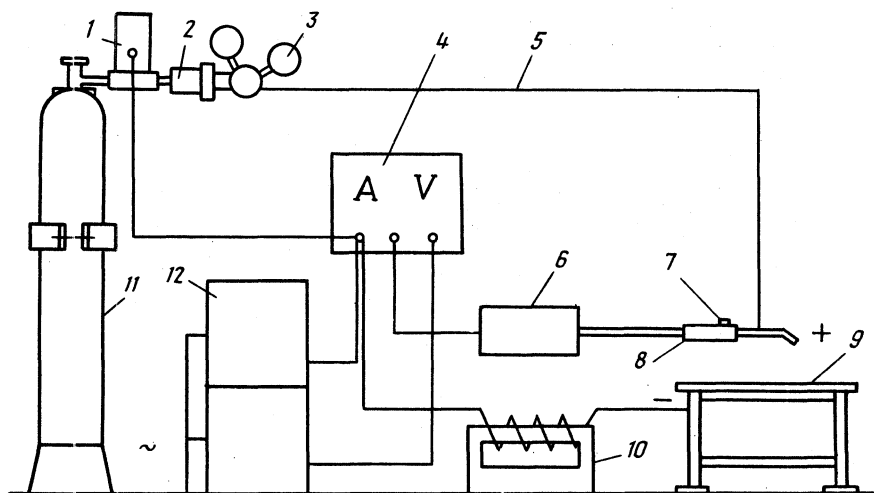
Схема оборудования для полуавтоматической сварки в среде углекислого газа:
